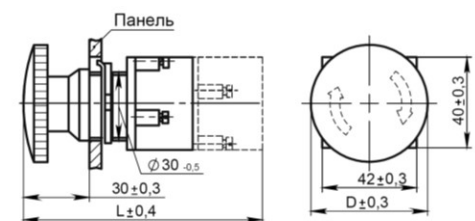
Габаритные размеры выключателей с грибовидным толкателем
